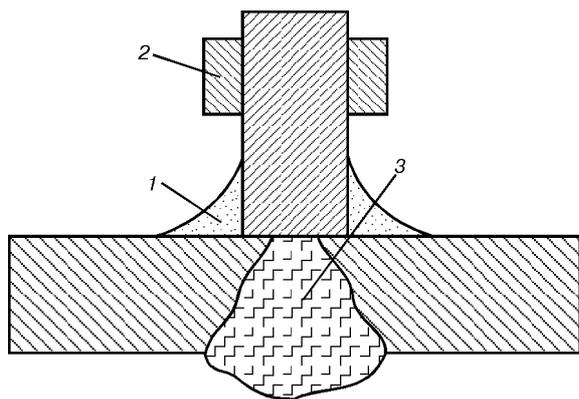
Схема сварно-паяного таврового соединения: 1 — галтель паяного шва; 2 — припой; 3 — сварной шов
